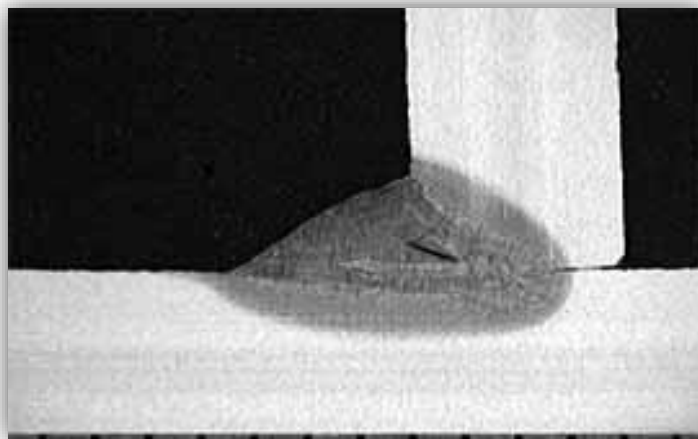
Defecto de solidificación en una unión tipo filete empleando soldadura híbrida con láser Nd: YAG y MAG. [29]
